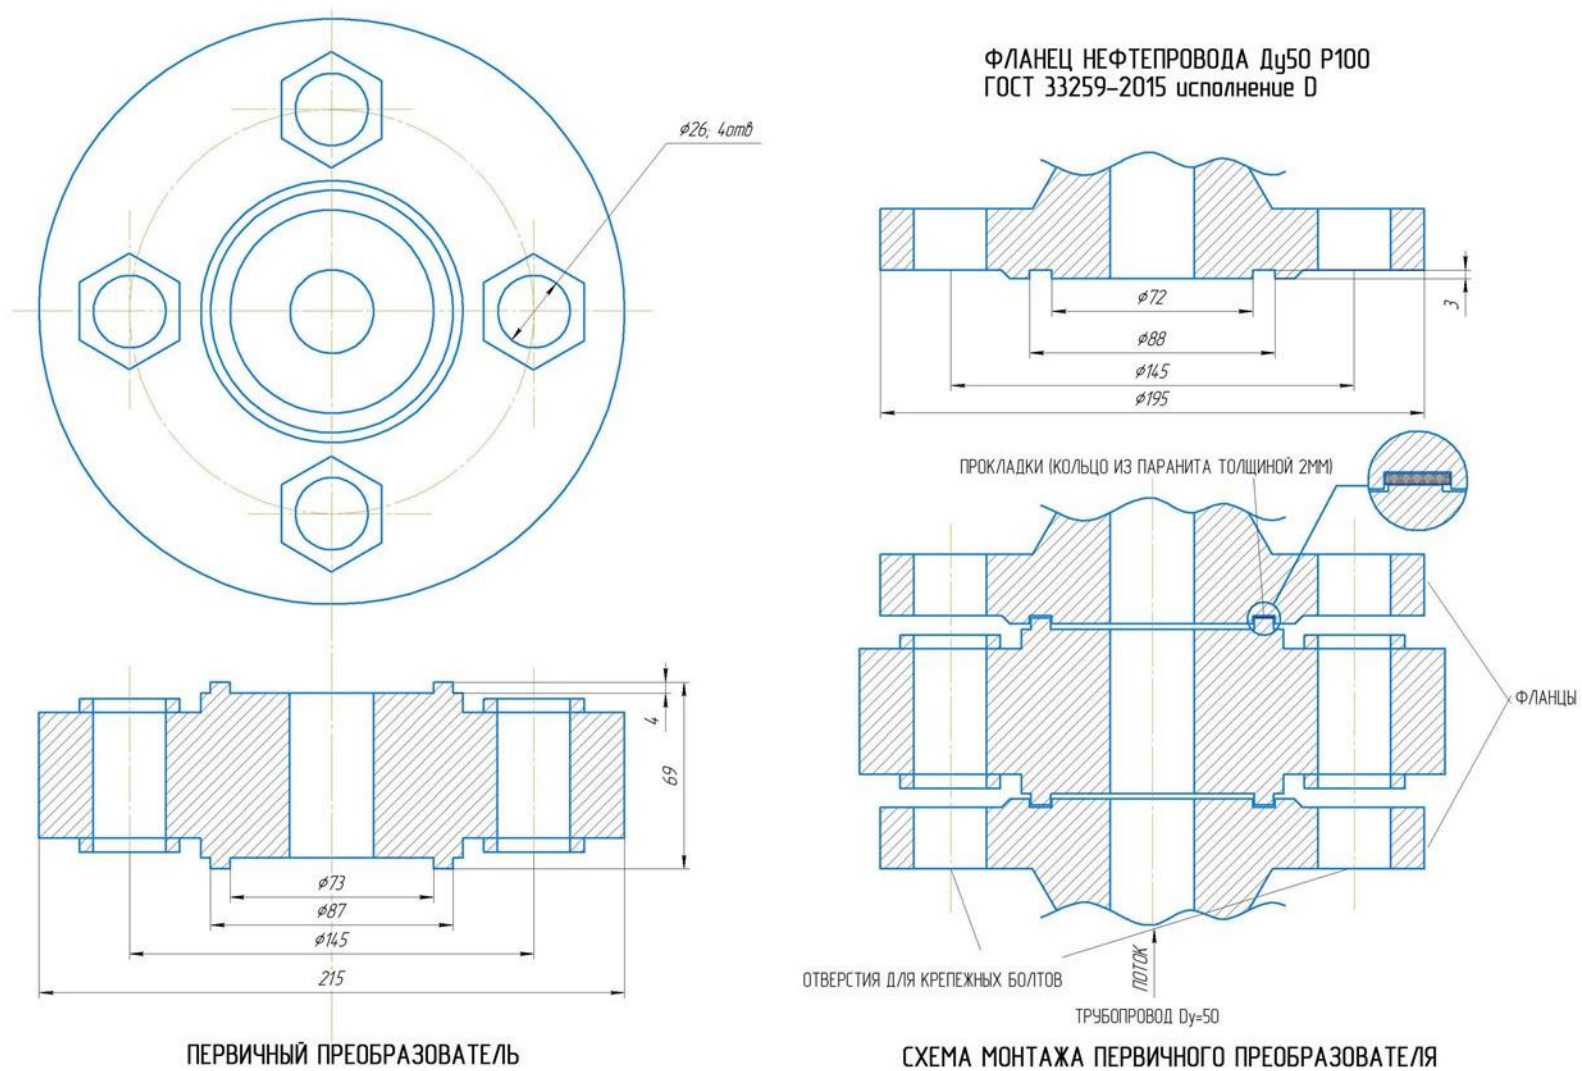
Габаритные и присоединительные размеры УДВН-2п для исполнения P100
